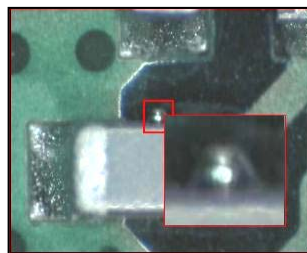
Defecto por presencia de esferas de soldadura
